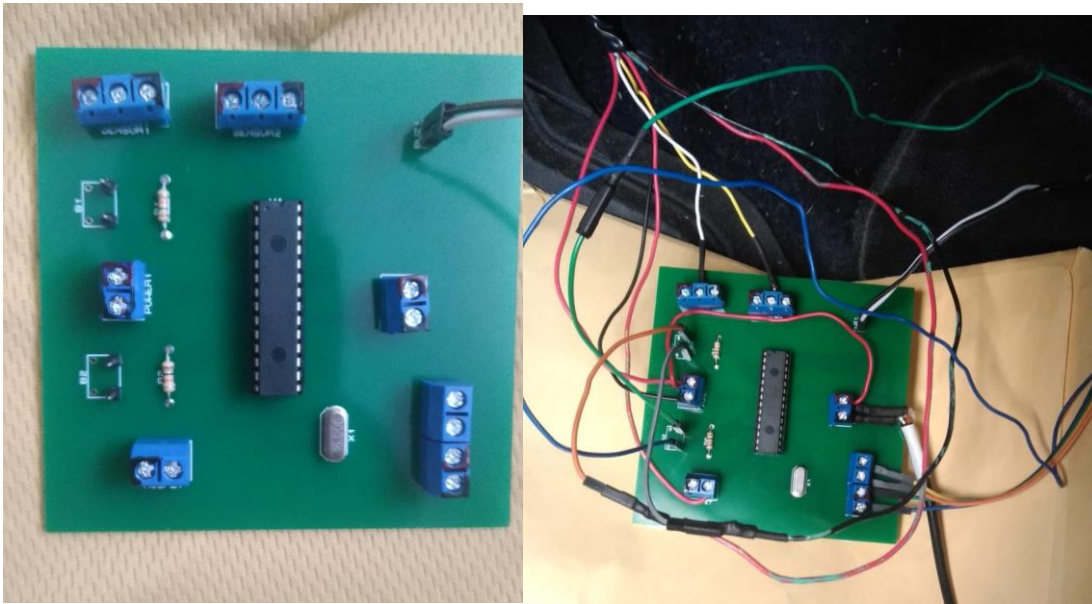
Circuito soldado y montado en la placa PCB
